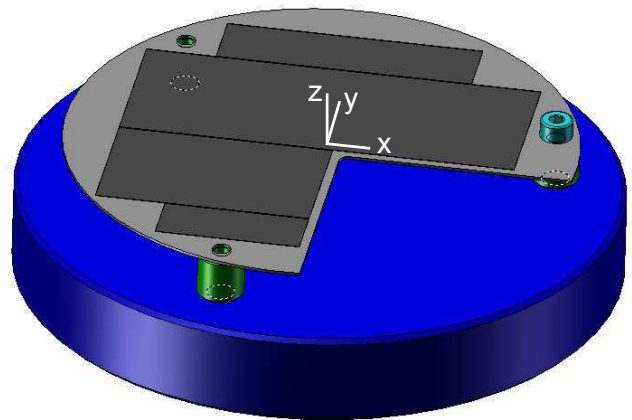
Dispositif de mise en position pour la mesure d'éprouvettes sur MMT ; les surfaces palpées apparaissent en gris foncé
